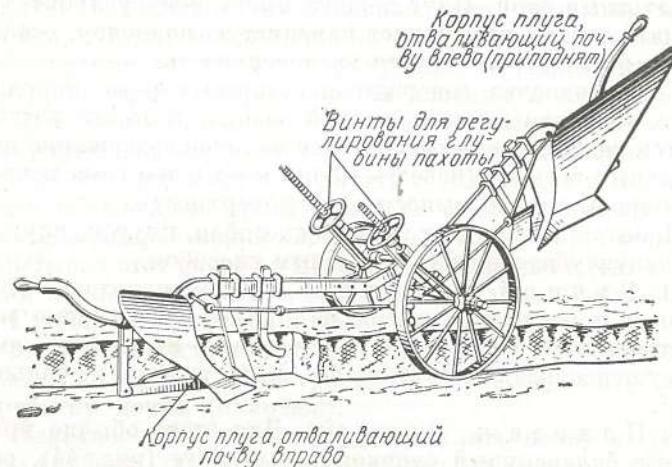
Балансирный плуг. Два симметрично расположенных корпуса плуга попеременно используются для отваливания почвы то вправо, то влево. Замена одного корпуса другим производится путем наклона нужного корпуса по отношению к оси колес. Глубина пахоты регулируется при помощи двух бесконечных винтов, снабженных маховиками.
